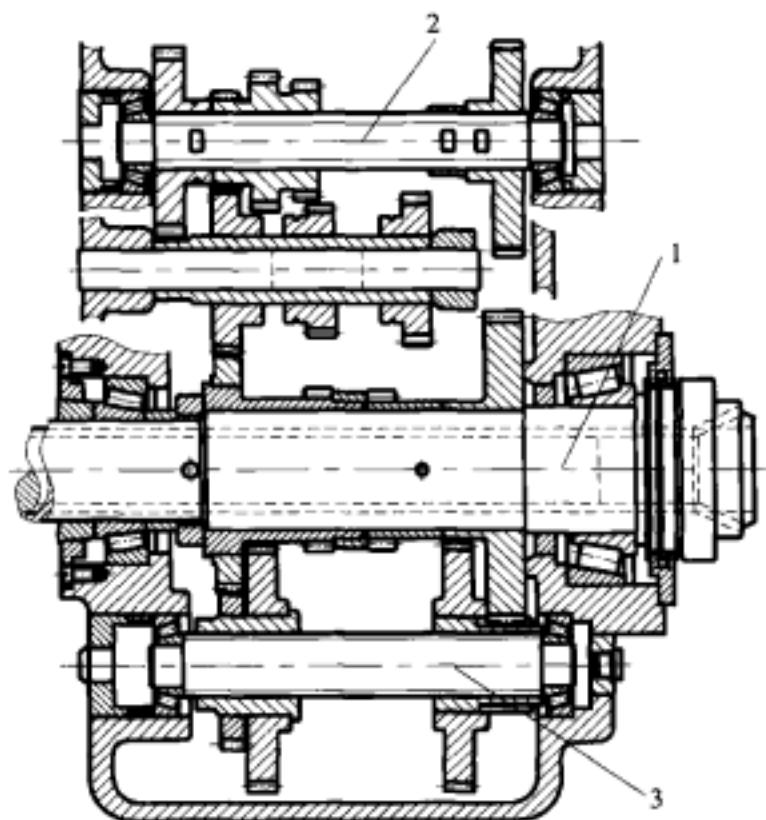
某机床变速箱轴系轴承结构(两端圆锥滚子轴承)。
